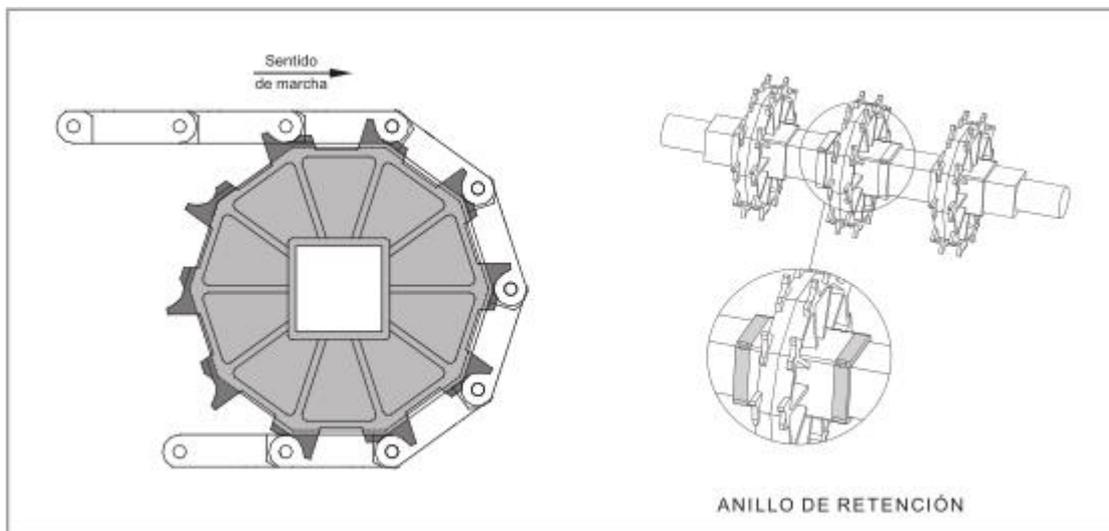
Engranajes para eje cuadrado y anillos de retención EUROBELT serie E50.
